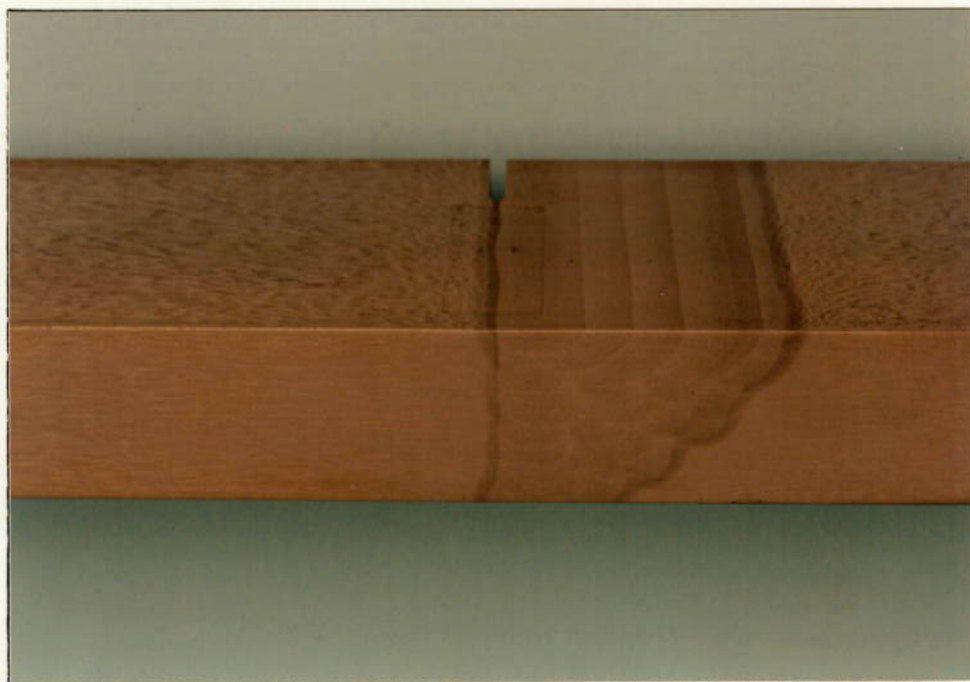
Detalhe do entalhe de um CP CTOD (aço 2 soldado) atacado com reativo para macrografia.
